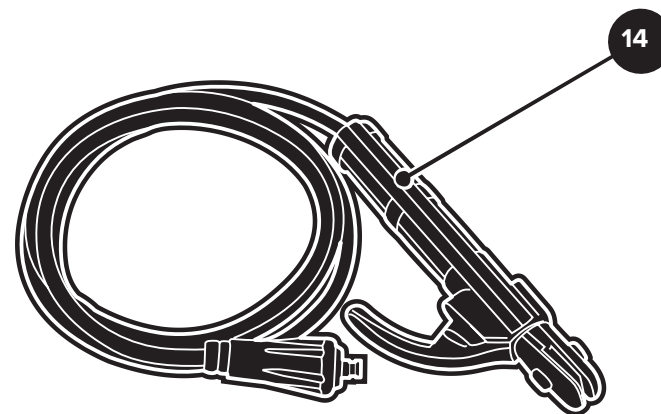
Сварочный кабель с электрододержателем
